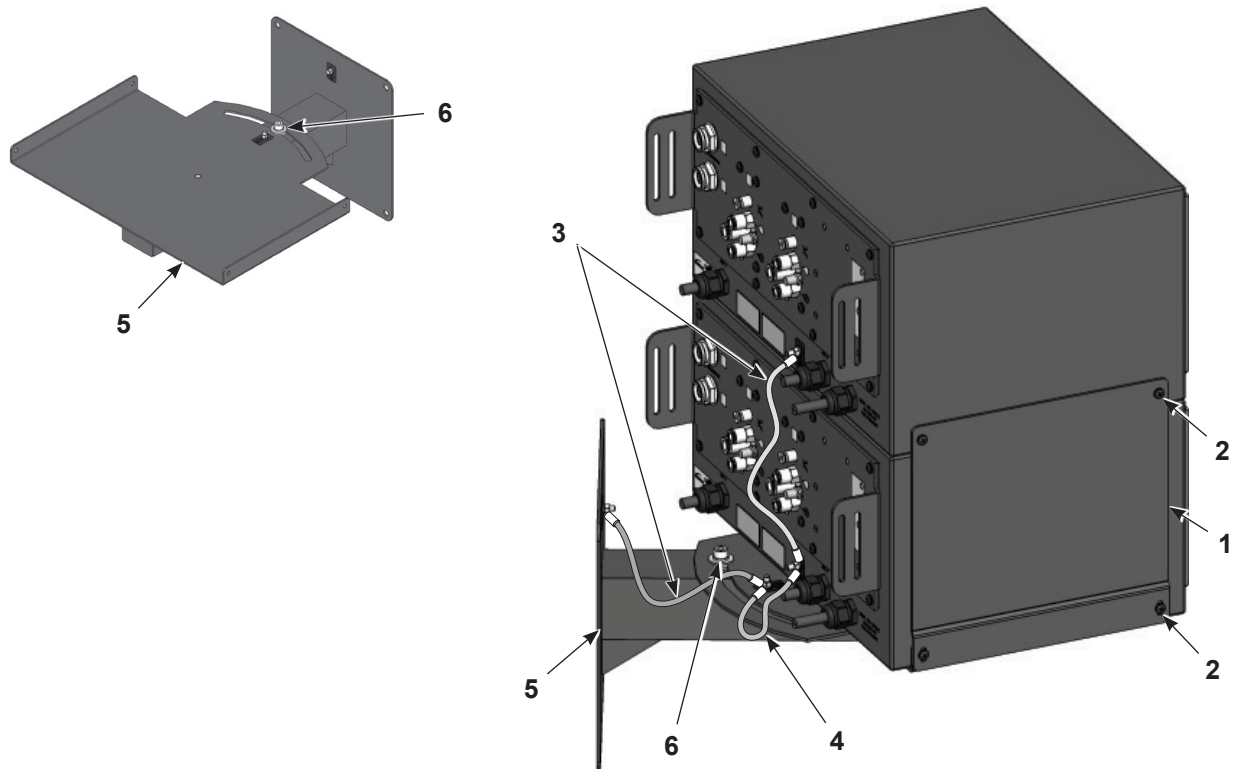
Montaje del controlador doble con soporte opcional de montaje en pared
